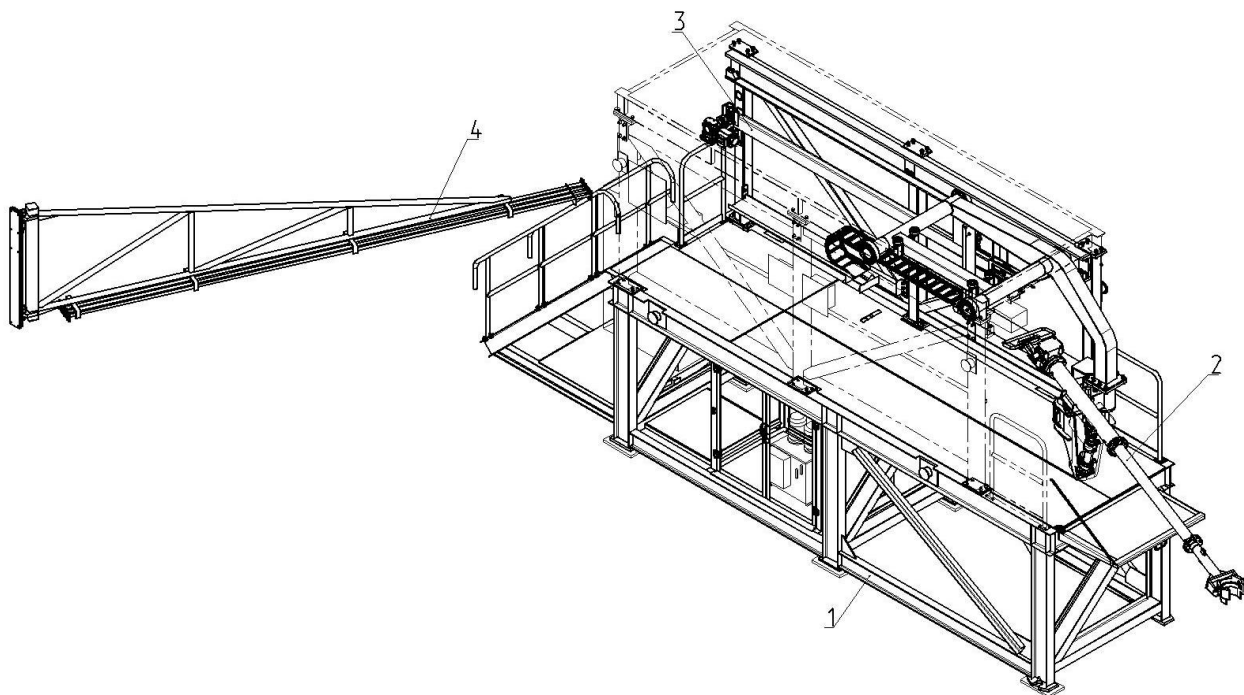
Маніпулятор приводу обертального захвату: 1 – майданчик; 2 – пристрій для встановлення обертального захвату; 3 – привід; 4 – поворотний кронштейн
